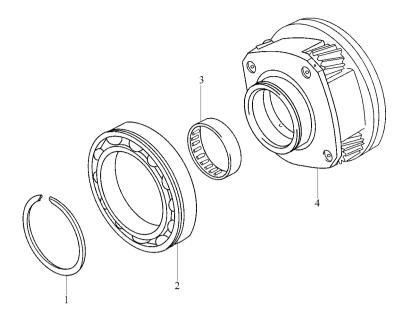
行星齿轮零件分解图 1—弹簧卡环 2—外轴承 3—内轴承 4—行星齿轮部件
